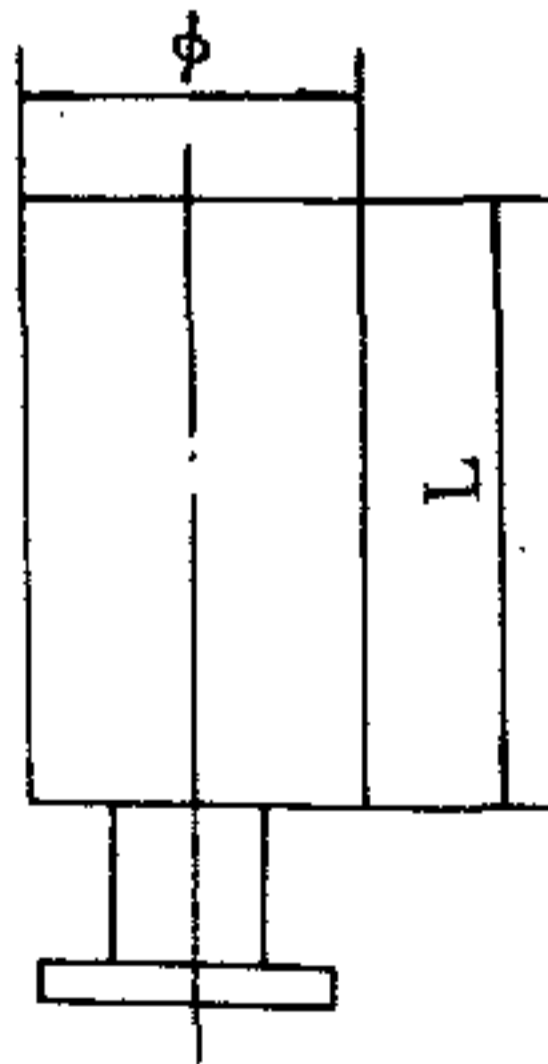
HP-QP-3 型排气放空消声器外形示意图
